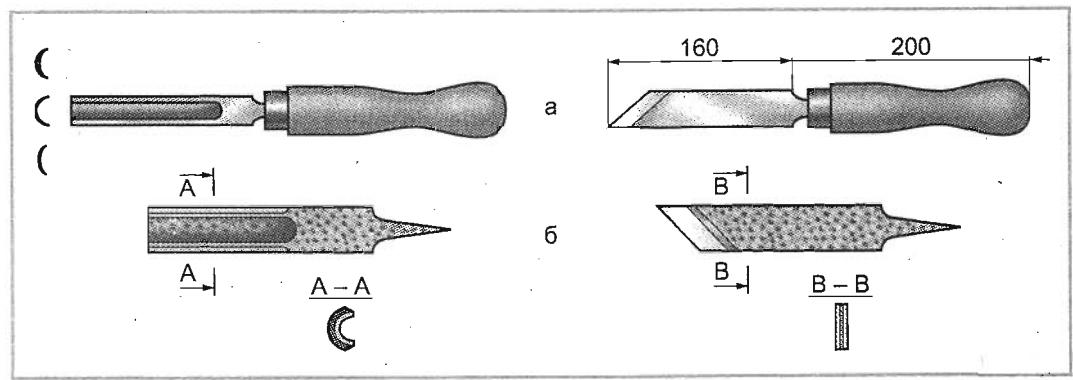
Инструмент для токарных работ: а – рейер и мейсель, изготовленные из круглого и плоского напильников; б – рейер и мейсель, изготовленные из стальных пластин и полотен механической пилы точечной сваркой и ковкой
